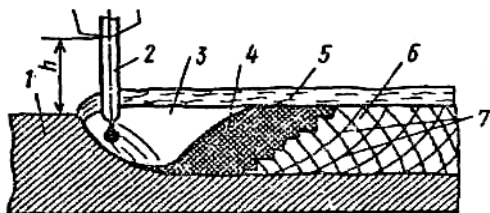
Плавильное пространство при сварке под флюсом: 1 — основной металл; 2 — электродная проволока; 3 — передняя часть сварочной ванны; 4 — хвостовая часть сварочной ванны (жидкий металл); 5 — флюс; 6 — закристаллизовавшийся сварной шов; 7 — границы кристаллизационных слоев,  $h$  — вылет электрода
